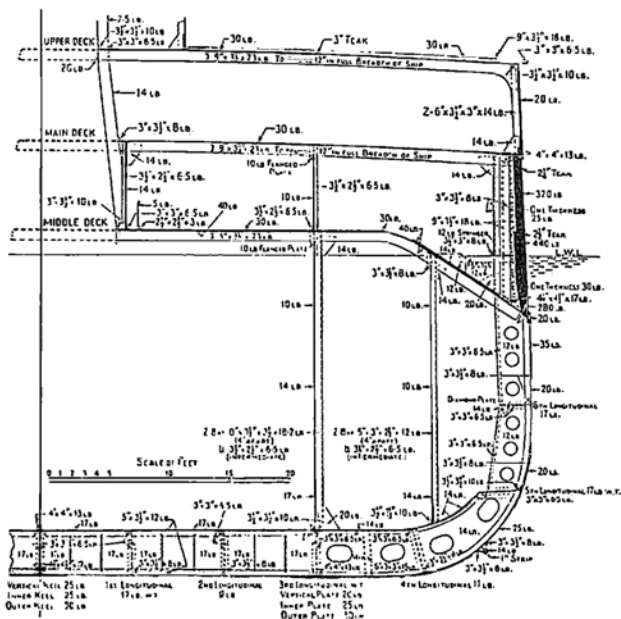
Чертеж конструкции *H.M.S. Dreadnaught* (1906) показывает только половину сечения корпуса, с номерами элементов и их расположением (Приводится с разрешения National Maritime Museum, Вашингтон).
